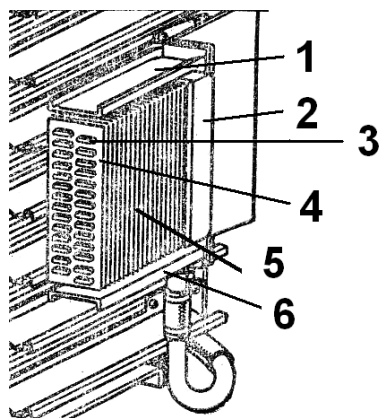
Устройство масляного радиатора: 1 и 6-опорные пластины; 2-бачки радиатора; 3-трубки; 4-наполнитель; 5-сердцевина.
